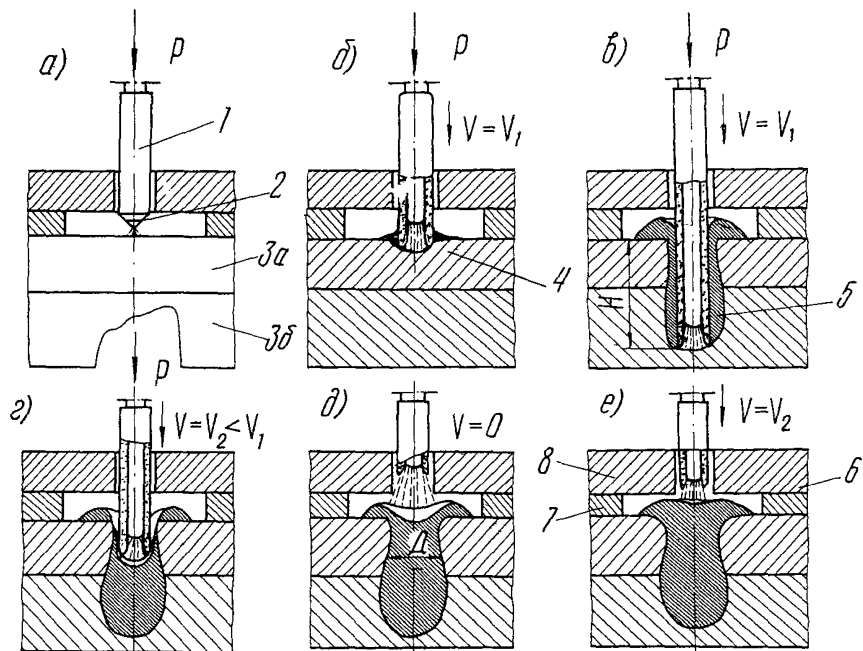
Схематическое изображение этапов полного цикла автоматической дуговой точечной сварки с принудительными проплавлением и формированием
